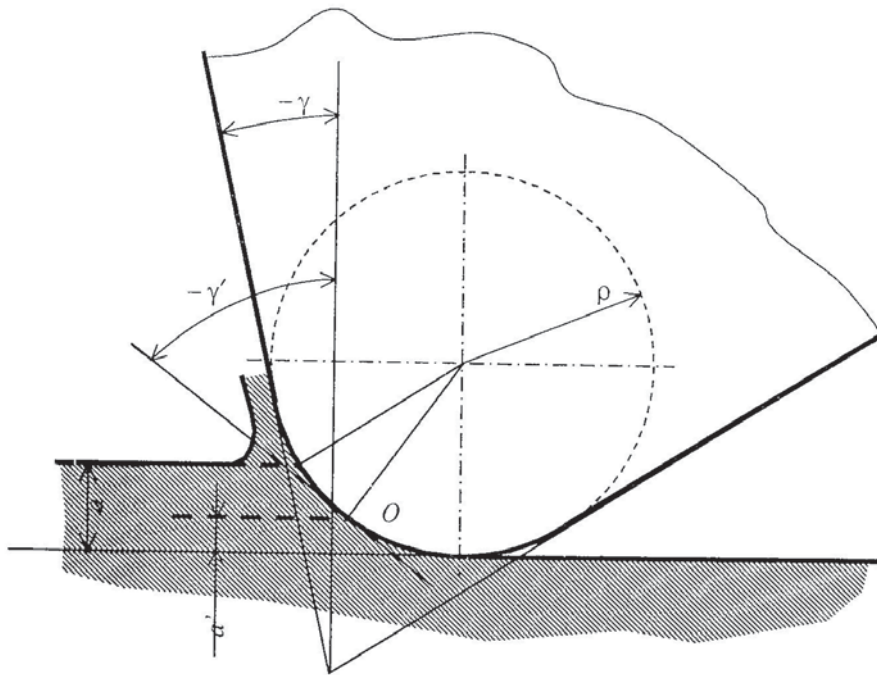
Схема взаимодействия с обрабатываемой поверхностью абразивного зерна, имеющего закругление кромки
